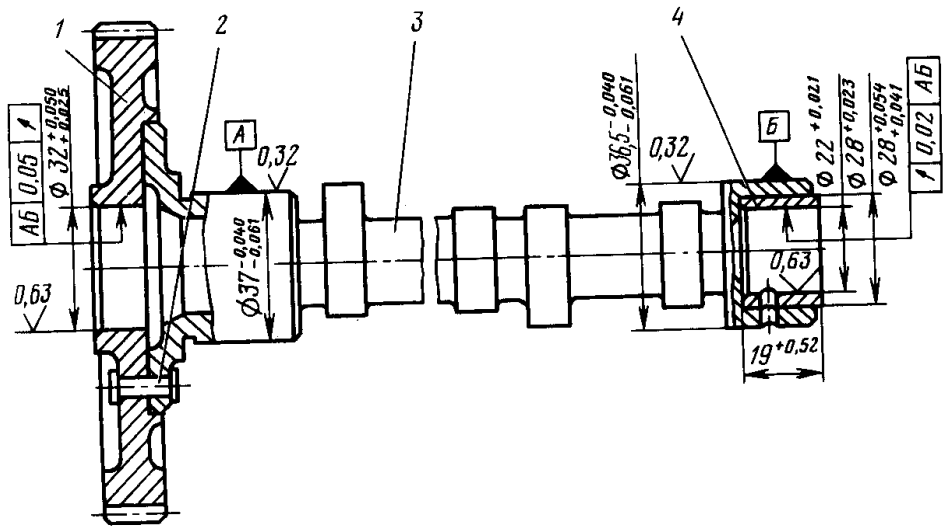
Распределительный вал в сборе: 1 — шестерня; 2 - заклепка; 3 — распределительный вал; 4 — втулка
